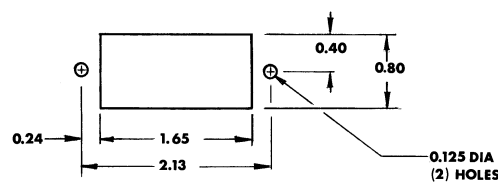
Dimensions de la découpe pour le montage en panneau LCD.
